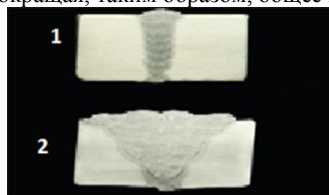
Сравнение сварных швов: 1 – (CRC-AW), 2 – (ручная дуговая сварка и механизированная сварка)
